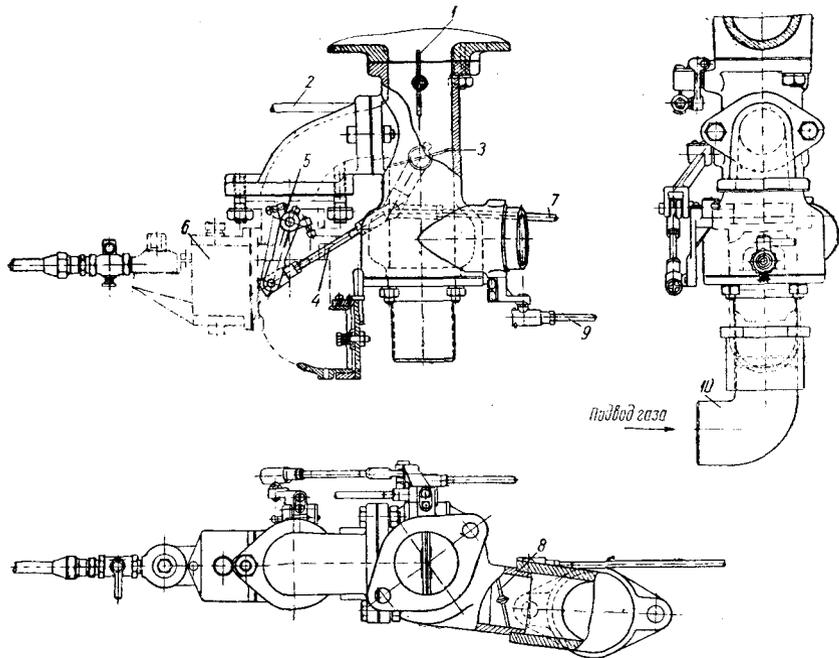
Смеситель двигателя трактора „сталинец-60“:
